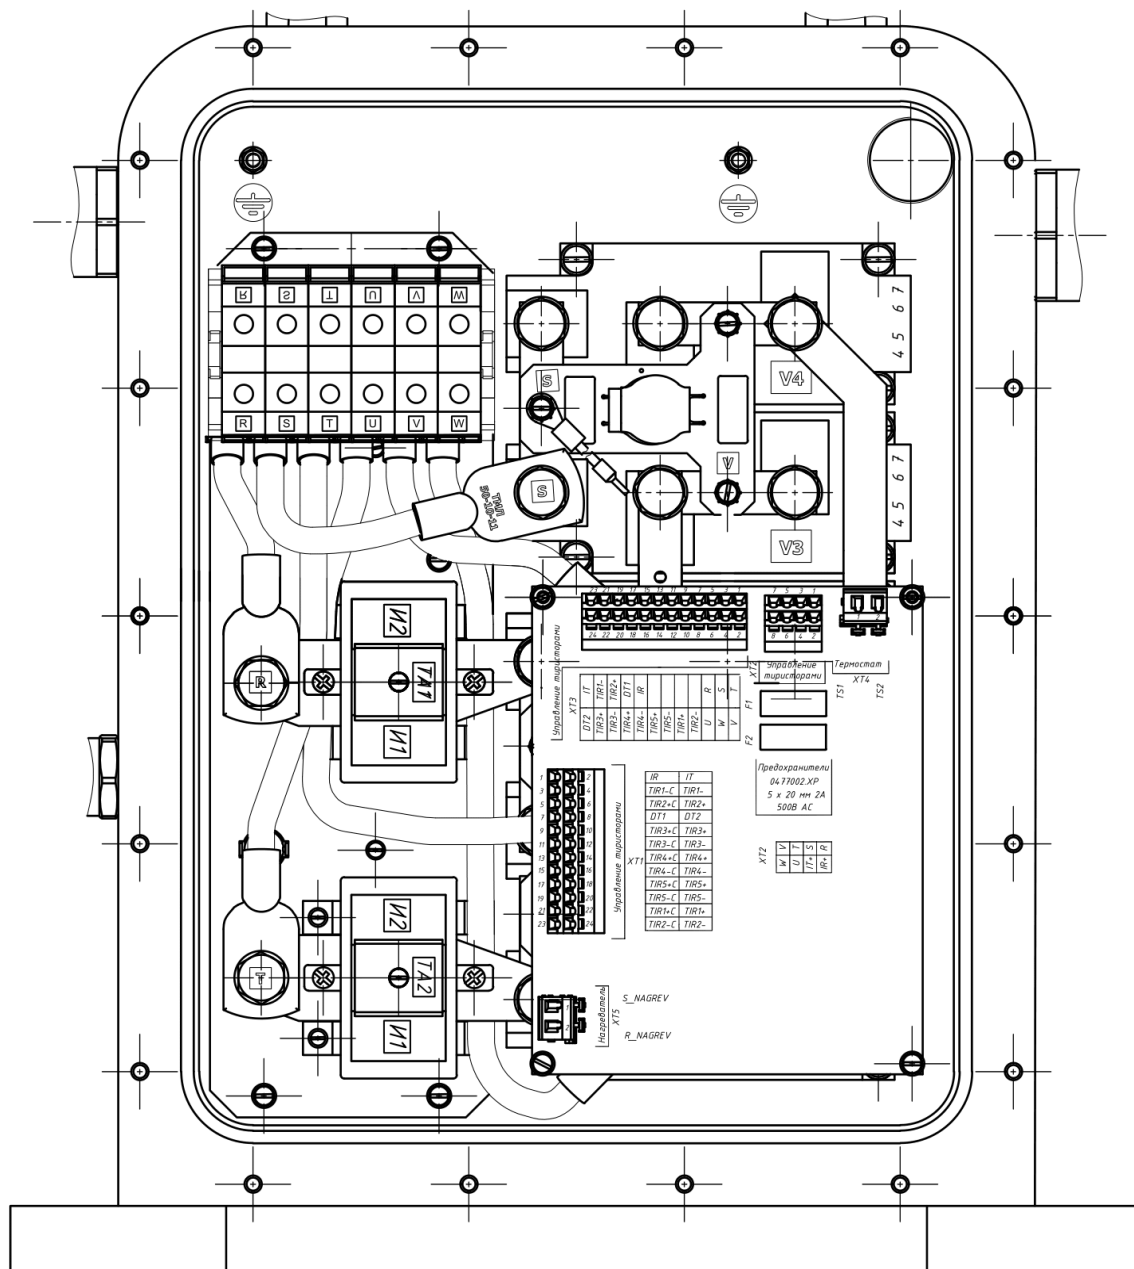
Типовой внешний вид бокса БСВ исполнений М15000, М20000, М32000
